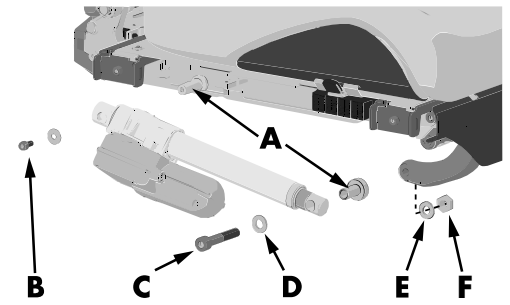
Die LINAK LA28-Stellvorrichtung für die Beinstütze wird von zwei Verschraubungen (B) und (C) gehalten.
